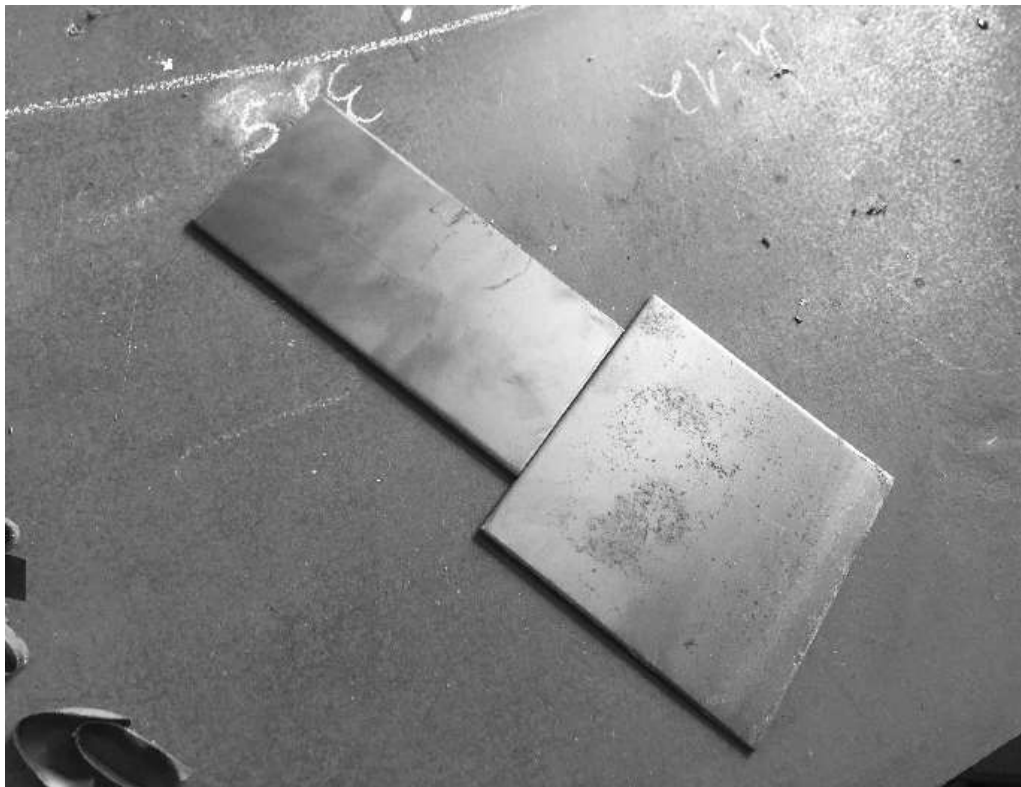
Imagem de solda em tons de cinza $B_c(x,y)$.
